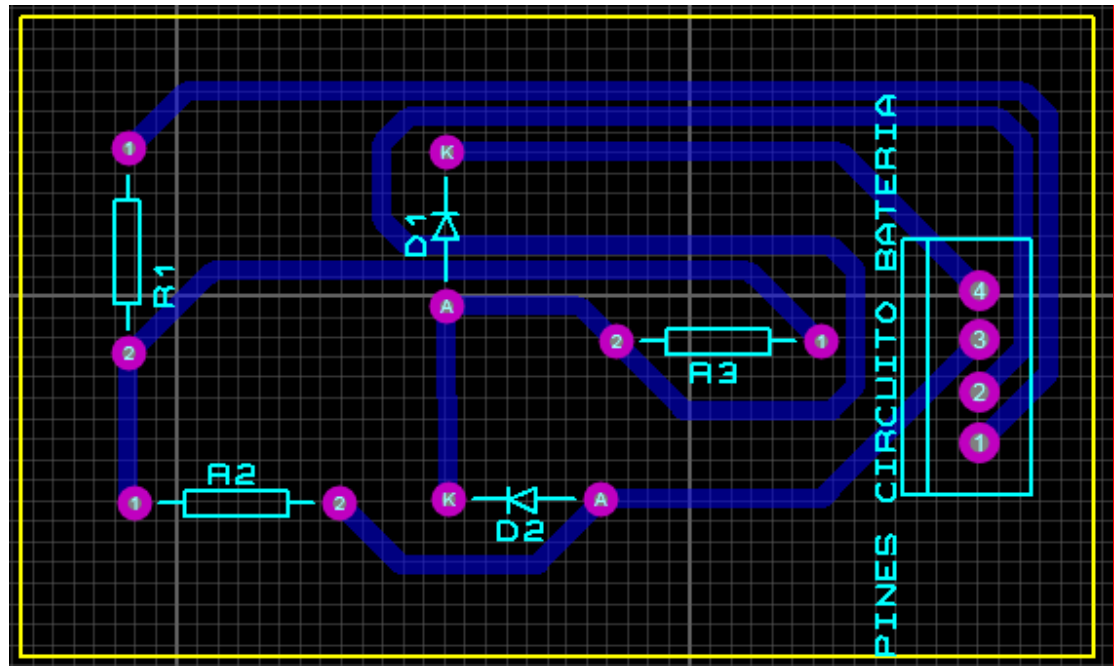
PCB Tarjeta circuito medidor de carga del prototipo diseñado en Proteus 8.
